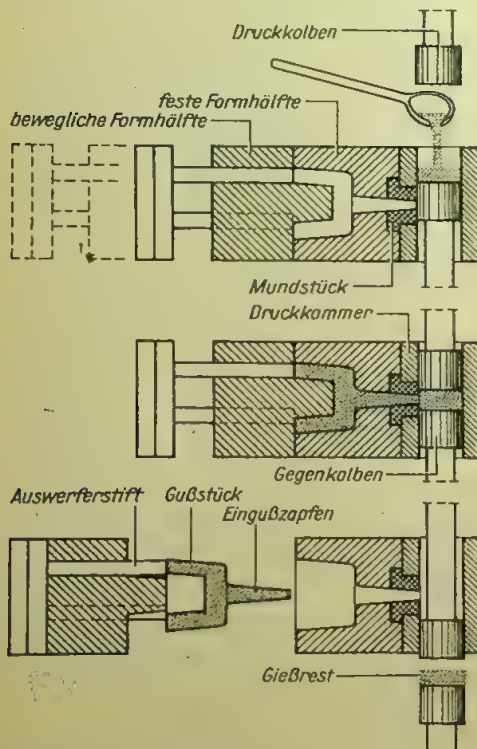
Druckgußverfahren mit senkrechter Kaltkammer
